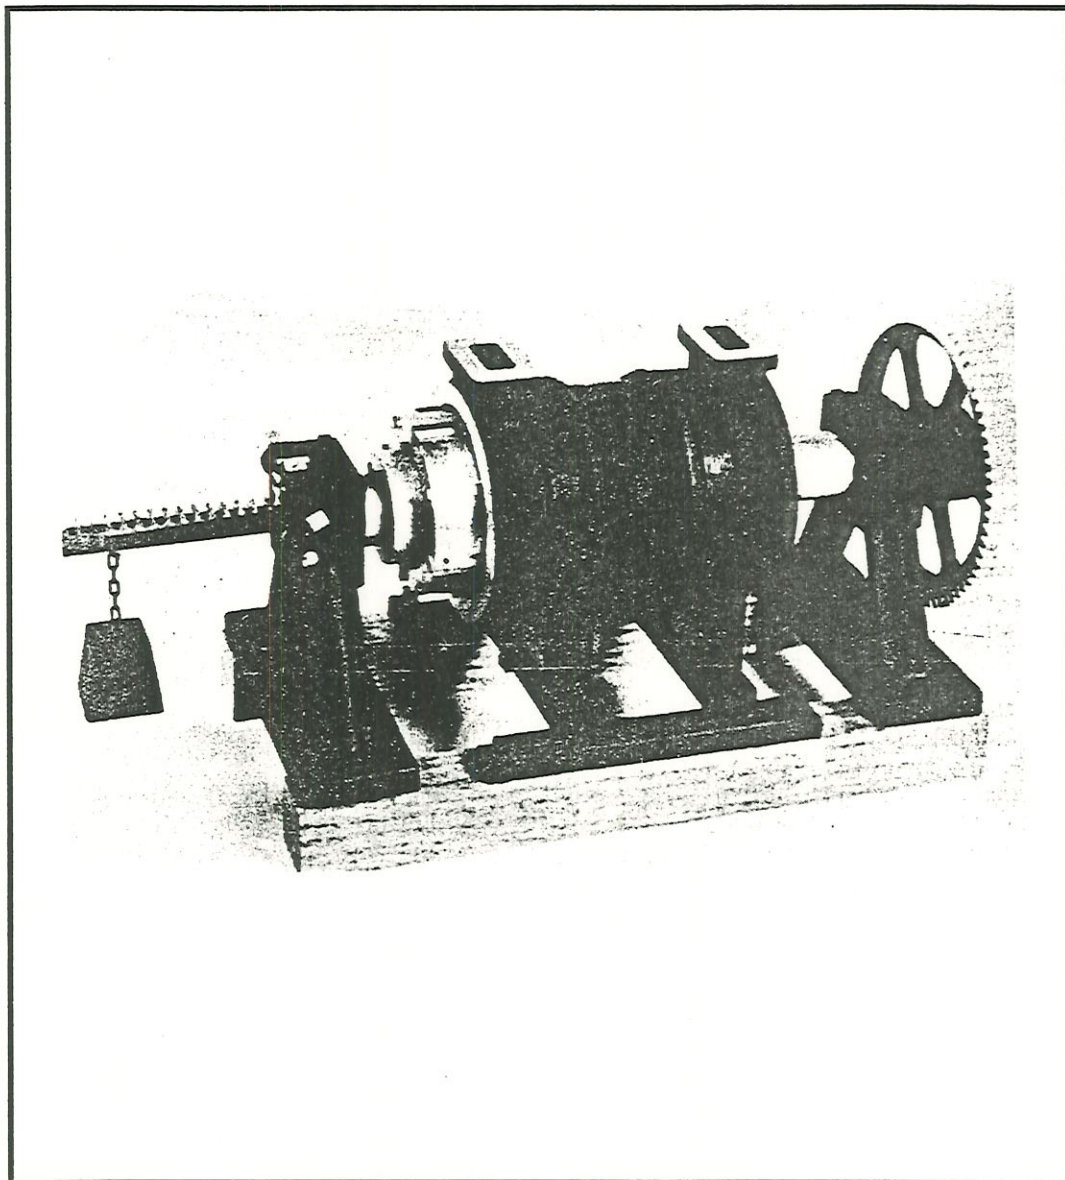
A primeira máquina-ferramenta básica: o torno mandrilador de John Wilkinson construído em 1.775 (KIBBE, 1.988).
